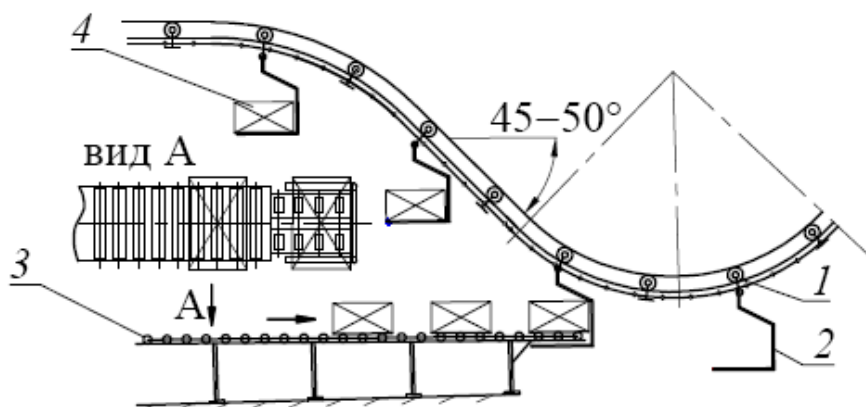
Схема автоматической загрузки подвешного грузонесущего конвейера
